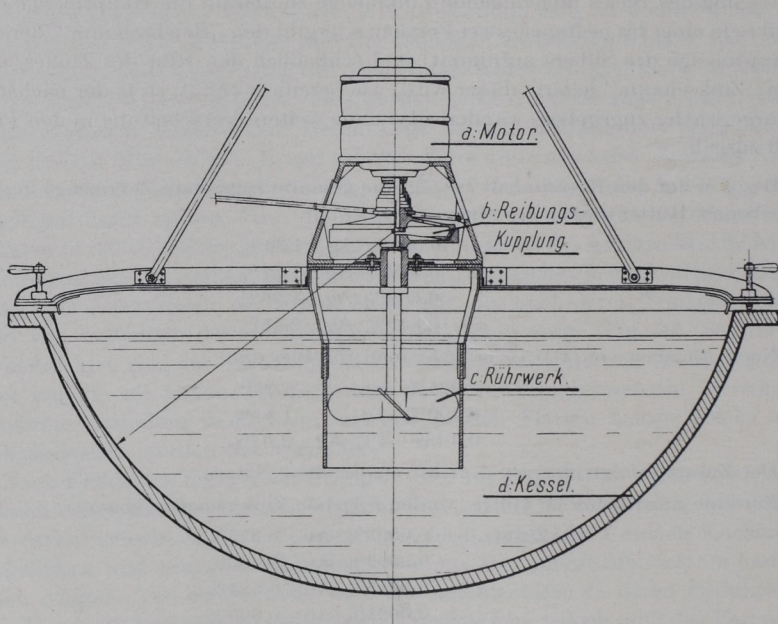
Howardscher Rührer mit direkt gekuppeltem Motor.
